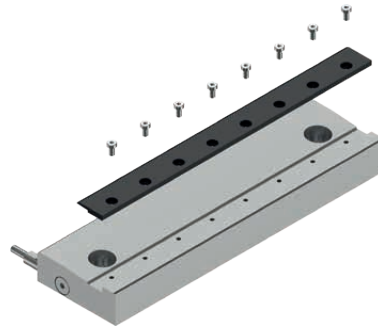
Endblock LMFC4-R-C-G zur Rückführung des Kühlmittels am Ende der Statoren-Bahn
